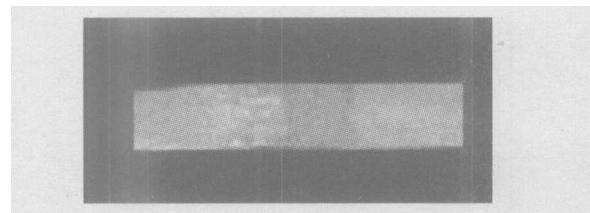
手工双面 TIG 焊焊接接头宏观试样
